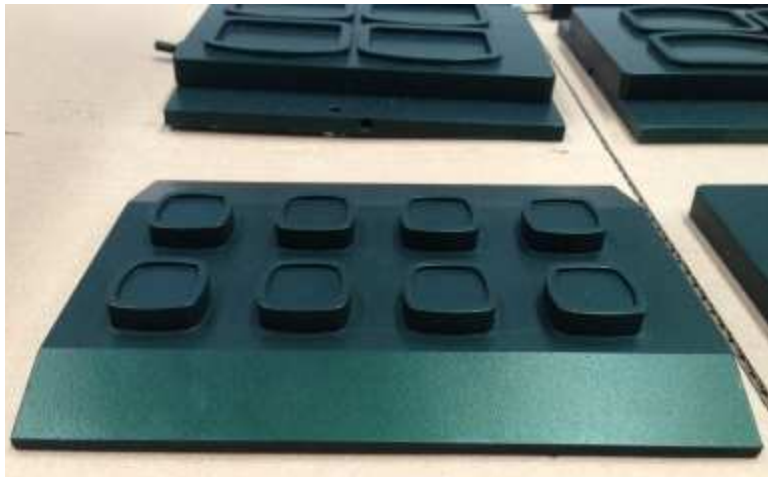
Placa de soldadura mecanizada con lóbulos que llevan un cordón perimetral.
